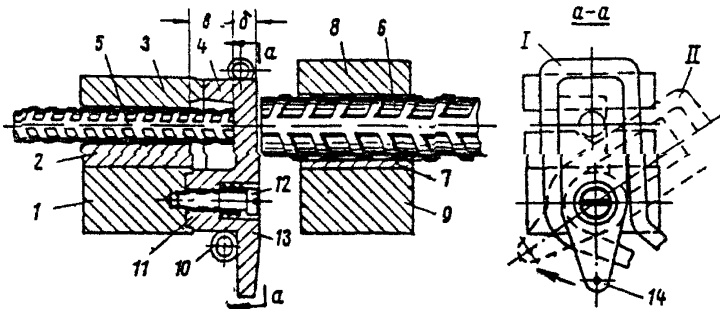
Схема модернизации серийной контактной стыковой машины для сварки стержней разных диаметров при 0,85 мм
